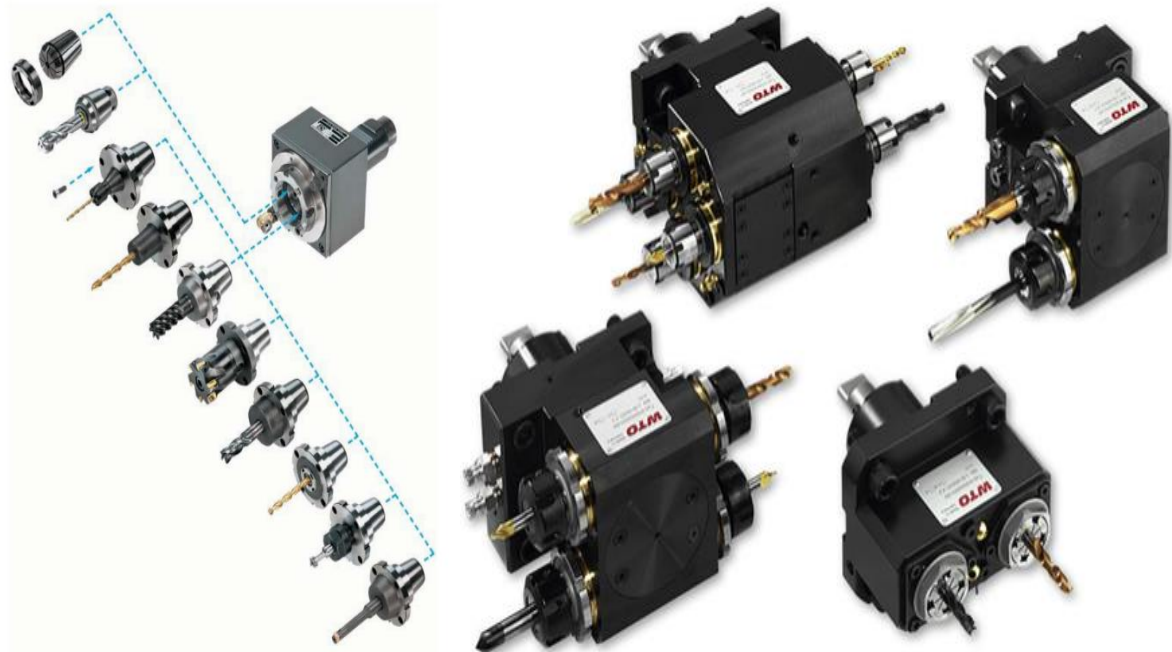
Модульный инструментальный блок (слева), многопозиционные инструментальные блоки (справа)
